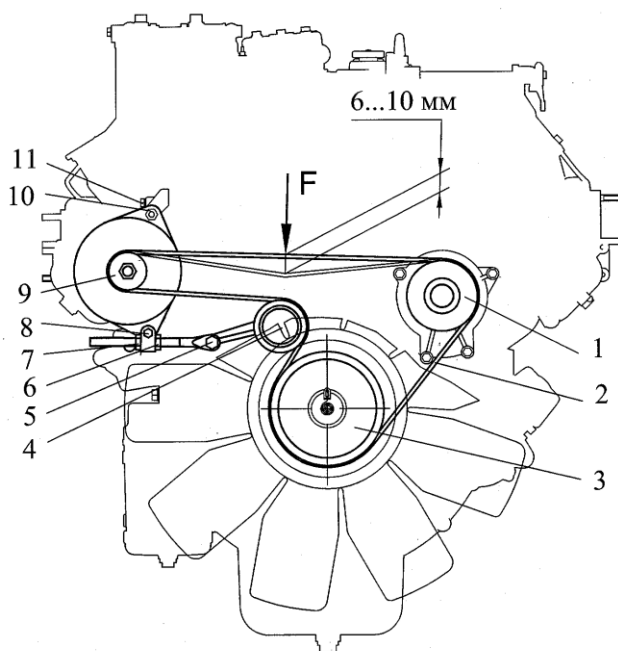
Схема проверки натяжения ремня привода генератора и жидкостного насоса: 1 - шкив жидкостного насоса; 2 - ремень поликлиновой; 3 - шкив коленчатого вала; 4 - натяжной ролик; 5, 8, 11 - болты; 6, 7, 10 - гайки; 9 - шкив генератора
